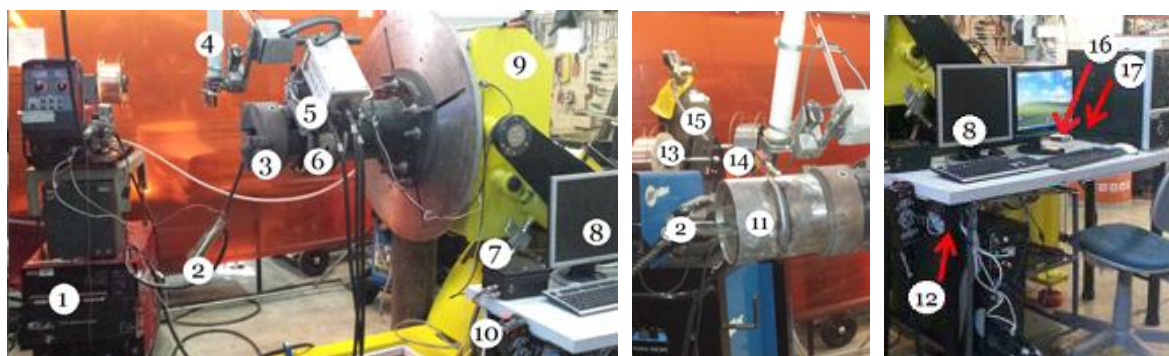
Bancada experimental utilizada, sendo: 1. Fonte de soldagem; 2. Cabo terra da fonte de soldagem (aterramento em ambos os lados do tubo); 3. Suporte do tubo teste (“castanha”); 4. Tocha de soldagem; 5. Carrinho de movimentação da tocha (Tartilope V4); 6. Cinta de suporte para movimentação angular do carrinho. 7. Sistema de controle de ajuste automático da DBCP; 8. Monitor de visualização dos parâmetros de movimentação da tocha; 9. Mesa posicionadora; 10. Controle manual de manipulação da tocha; 11. Tubo teste; 12. Sistema de controle do manipulador da tocha (Tartilope); 13. Arame ER70S-6 com 1,2 mm de diâmetro; 14. Sensor *laser*; 15. Cilindro de gás; 16. Placa de aquisição; 17. Sistema de aquisição de dados.
